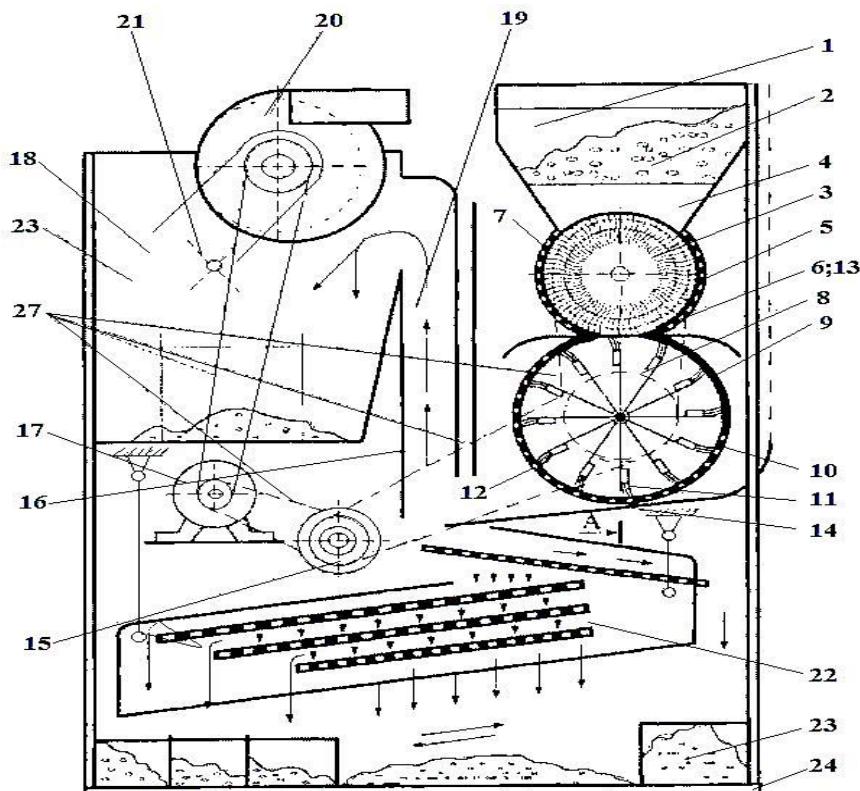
Схема универсальной малогабаритной семяочистительной машины непрерывного действия: 1 – загрузочный бункер; 2 и 3 – верхний и нижний отсеки загрузочного бункера; 4 – днище; 5 – шнеково-щеточный питатель; 6 и 13 – загрузочное и разгрузочное отверстия; 7 – сетчатая рабочая поверхность; 8 – обескрыливающий барабан; 9 – верхний полуцилиндр; 10 – нижний полуцилиндр; 11 – основные щеточные элементы; 12 – дополнительные щеточные элементы; 14 – разгрузочное окно обескрыливателя; 15 – приемный лоток; 16 – клиноременная передача; 17 – электродвигатель; 18 – осадочная камера; 19 – аспирационный канал; 20 – вентилятор; 21 – дроссельная заслонка; 22 – решетный стан; 23 – сборники семян; 24 – рама
